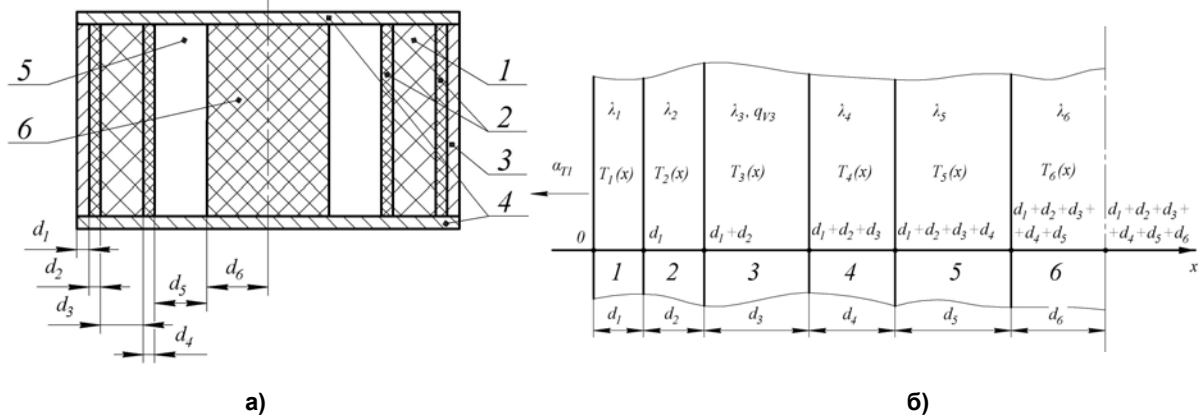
Схематичне зображення циліндричного ПЕП з додатковими конструктивними елементами (а) та його розрахункова модель (б)
